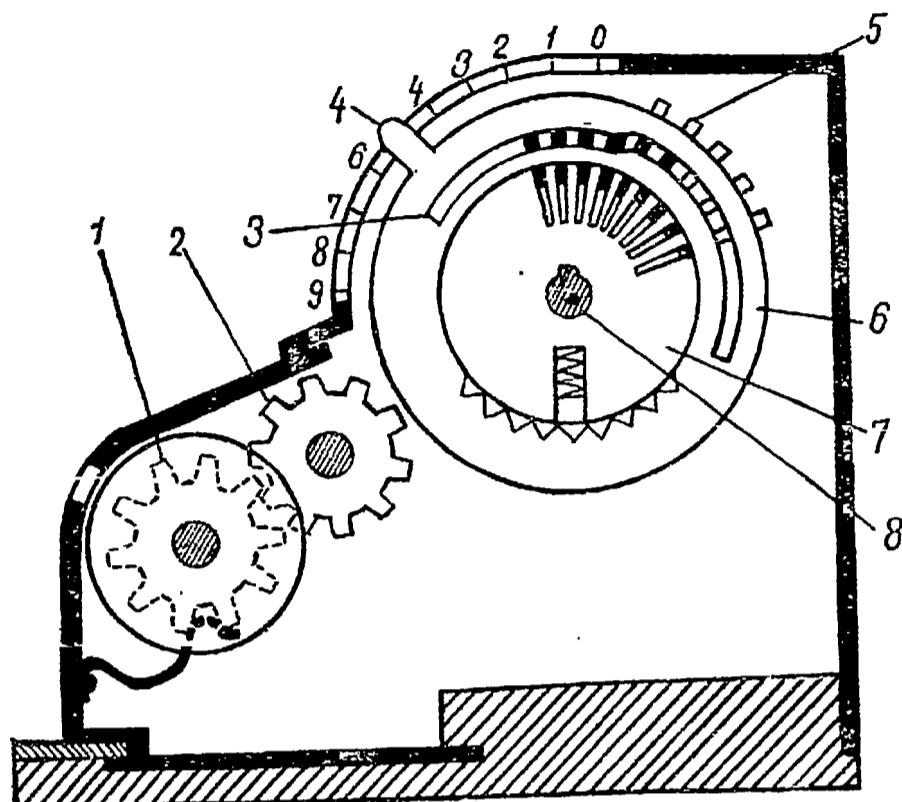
Схема конструкции вычислительных машин с колесом Однера:
